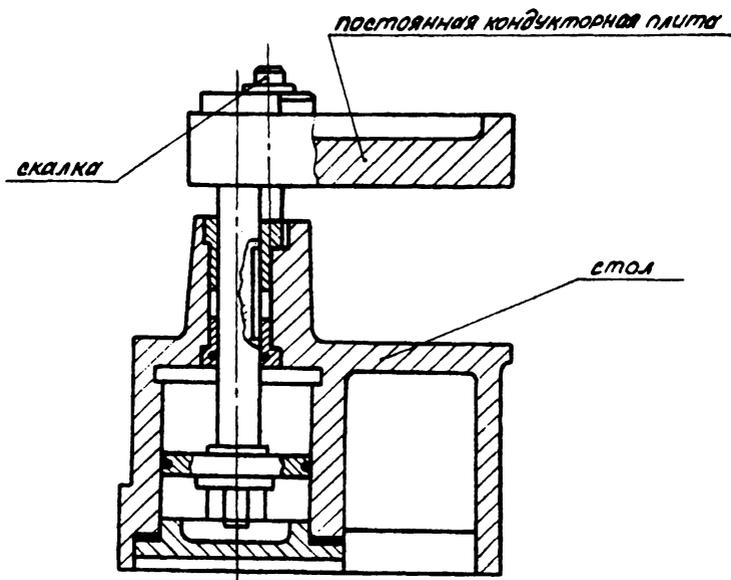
Скальчатый кондуктор консольного типа с встроенным пневмоприводом
